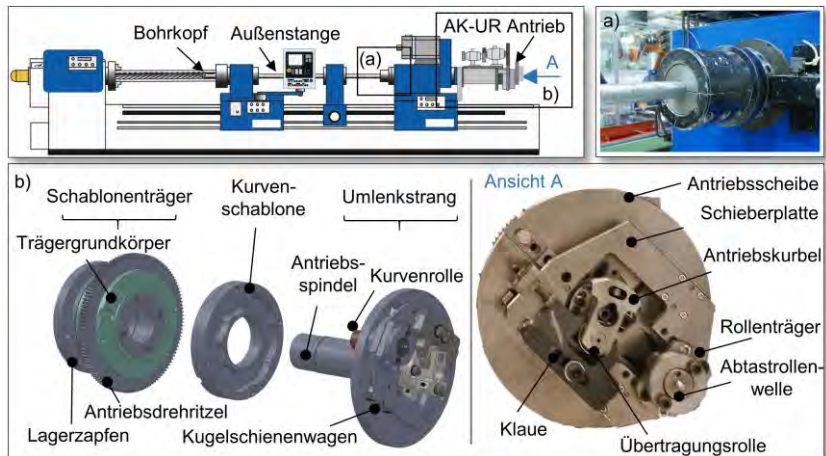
Montageposition des AK-UR-Antriebs; a) Bohrohraufnahme; b) Komponenten des AK-UR-Antriebs
